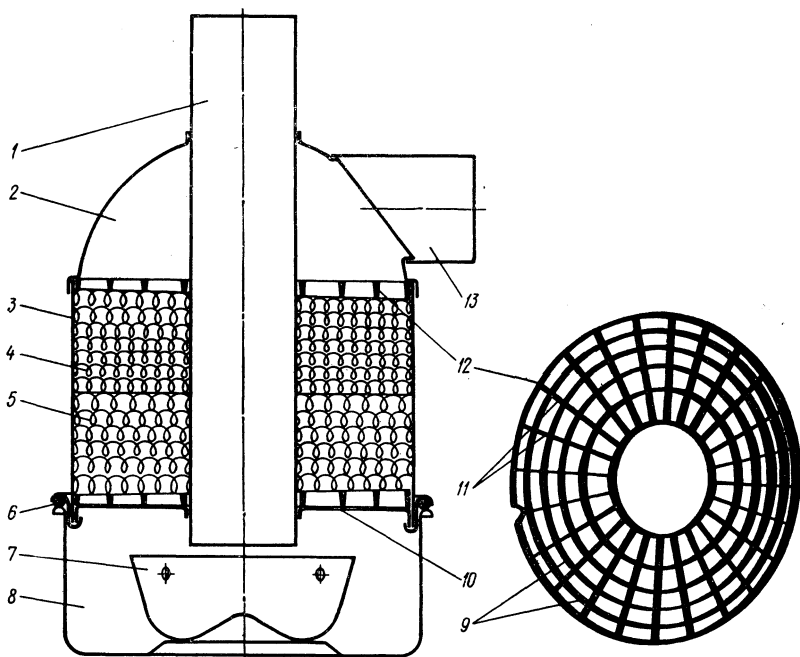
Усовершенствованный воздухоочиститель двигателя Д-50:
